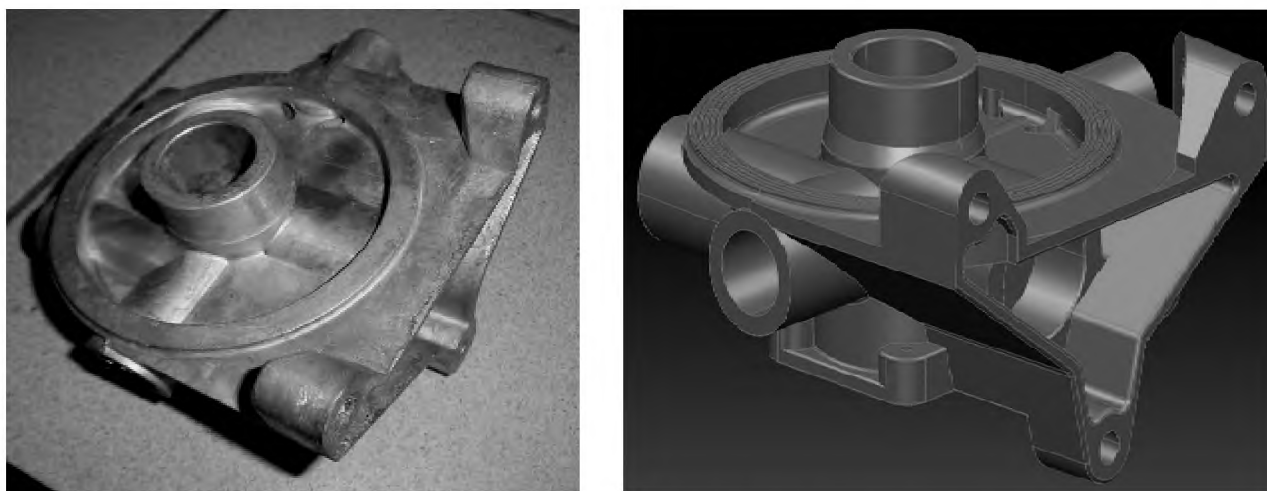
Литая заготовка и модель детали «Корпус адсорбера».
